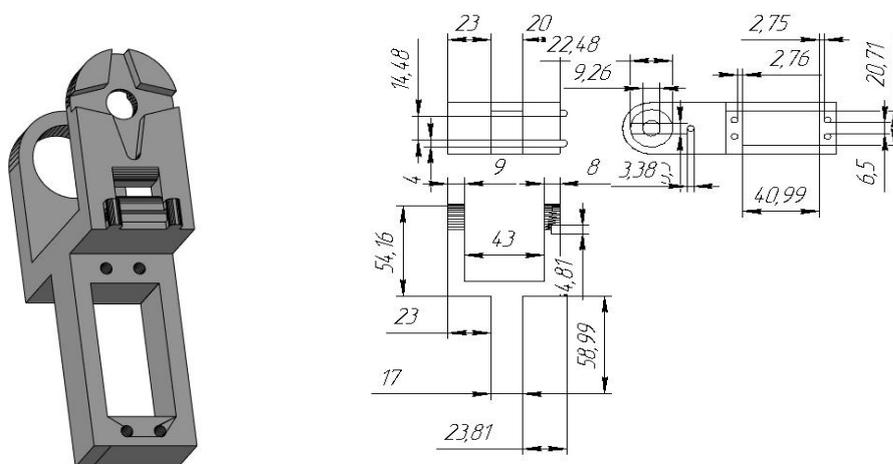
Модель и чертеж модуля конструкции корпуса.
